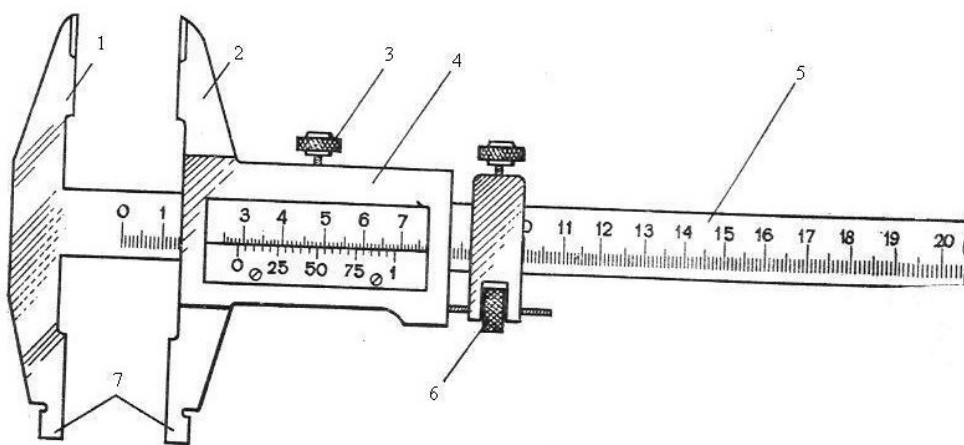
Будова штангенциркуля: 1 – нерухома ніжка, 2 – рухома ніжка, 3 – стопорний гвинт, 4 – рамка з ноніусом, 5 – лінійка, 6 – мікрометричний пристрій, 7 – ніжки для вимірювання внутрішніх розмірів
